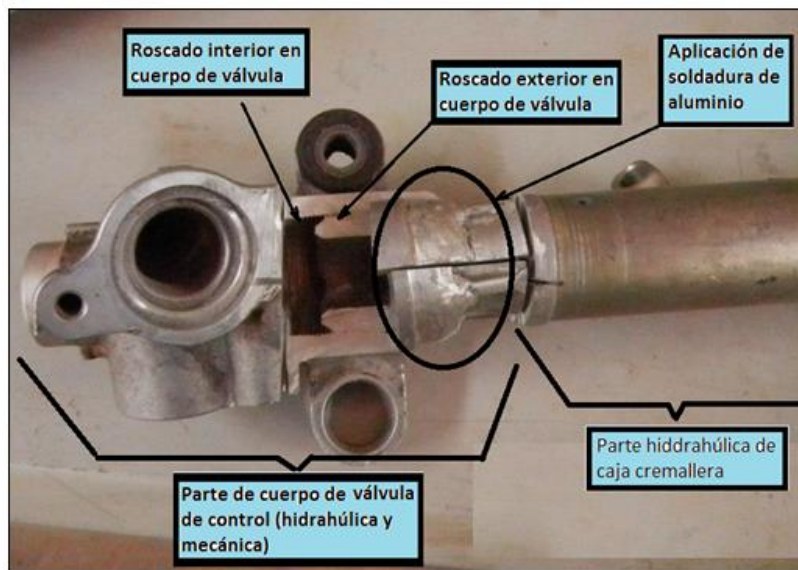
Aplicación de soldadura en caja rediseñada.
